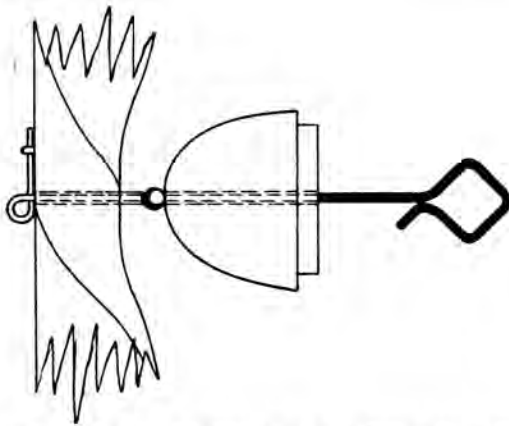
Zweckmäßige Ausführung der Luftschraubenwelle.
